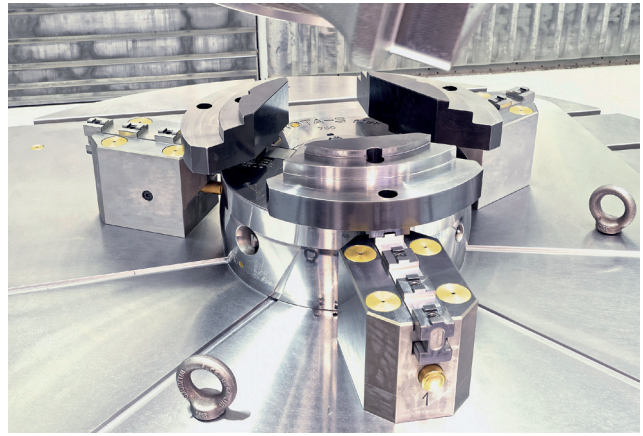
Ручной токарный патрон ROTA-S flex на 60% легче, чем стандартные токарные патроны и позволяет работать с заготовками самого разного диаметра
